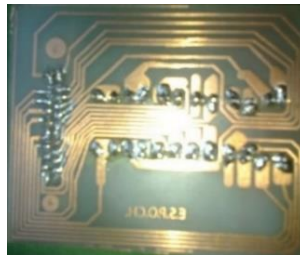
Montaje y soldado de la bornera que se conecta al PLC.
